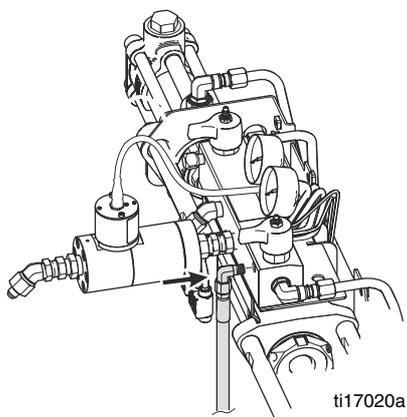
Raccordement du flexible sur le collecteur de fluide
